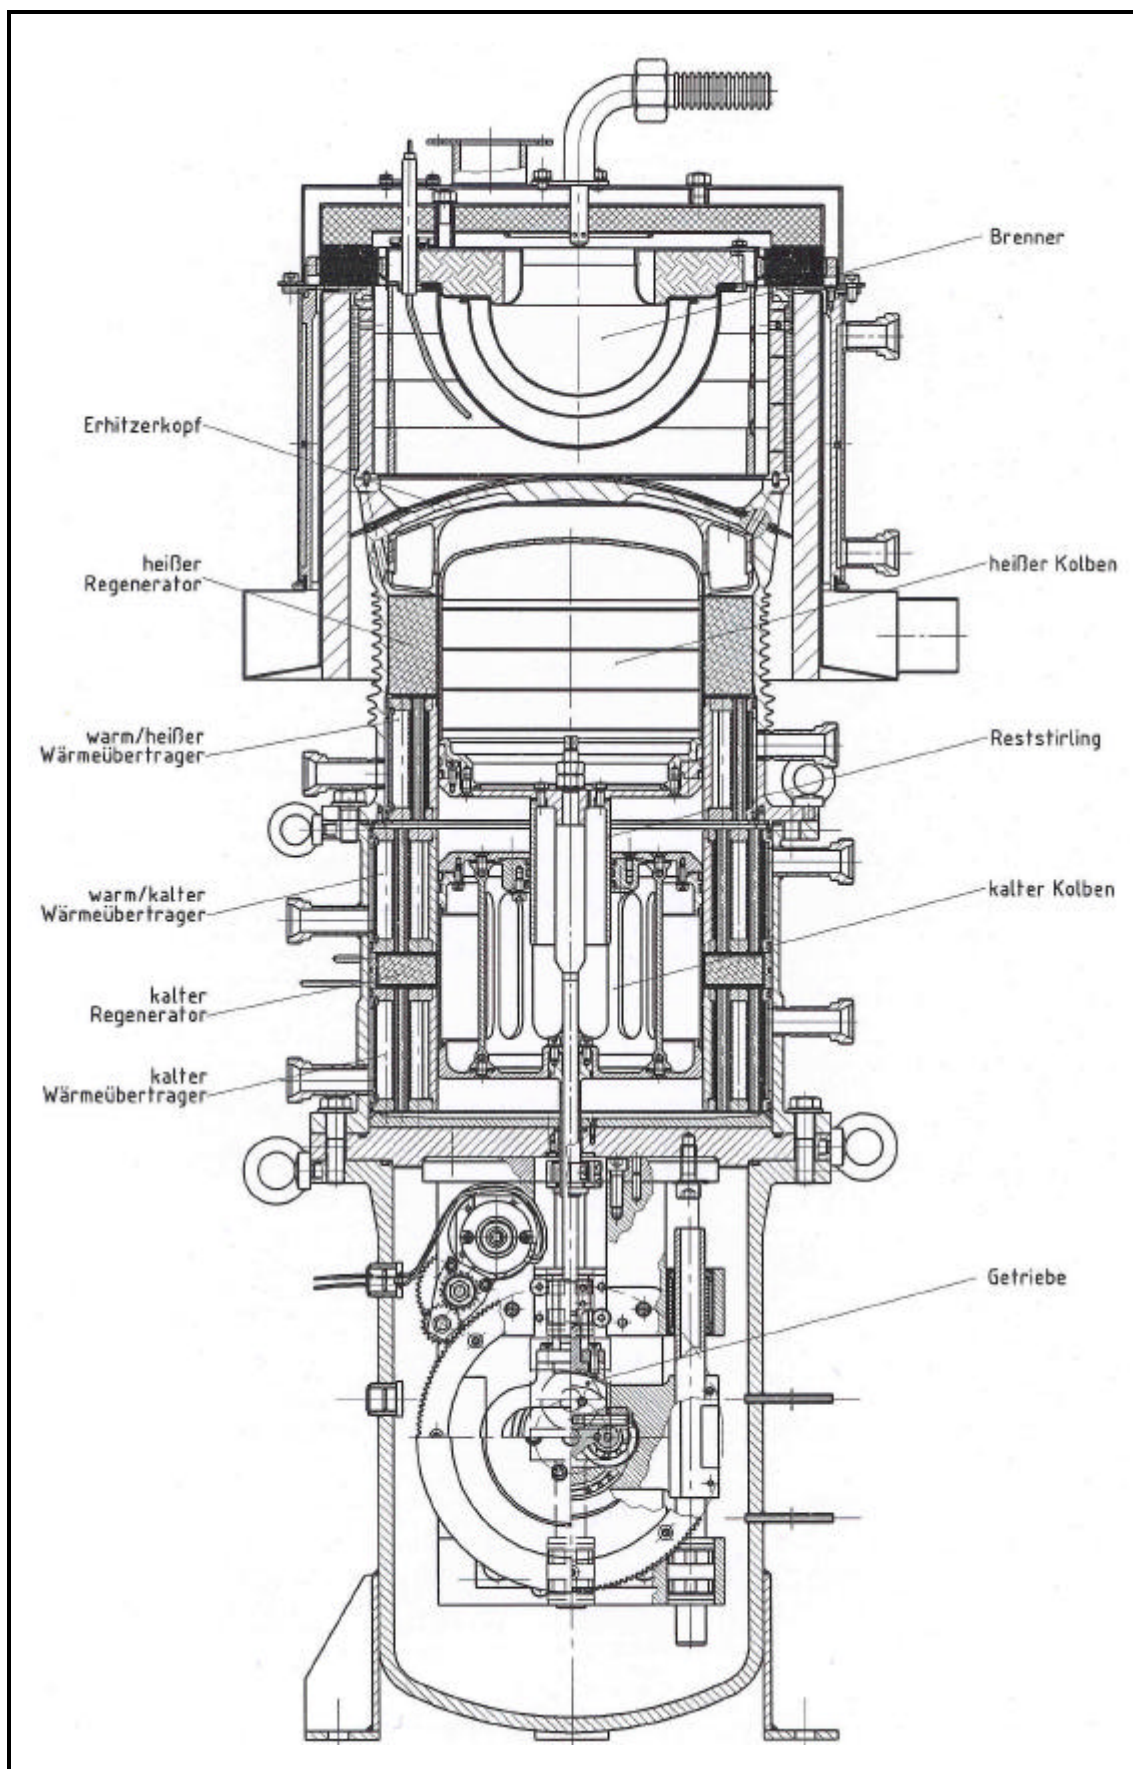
Schnittzeichnung der 20 kW Vuilleumier-Wärmepumpe.
